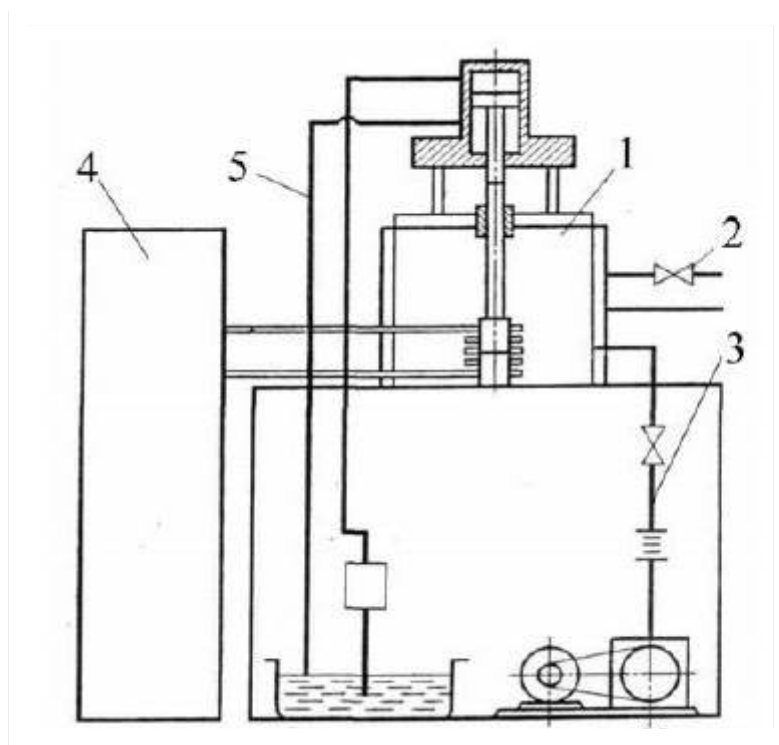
Принципиальная схема установки для диффузионной сварки [24]
